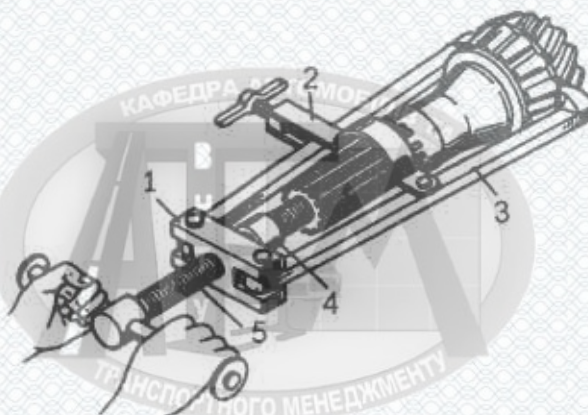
Випресування зовнішнього кільця підшипника зі стакану підшипників ведучої конічної шестерні [11]
